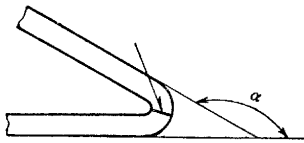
Схема испытания сварного соединения на статический изгиб
